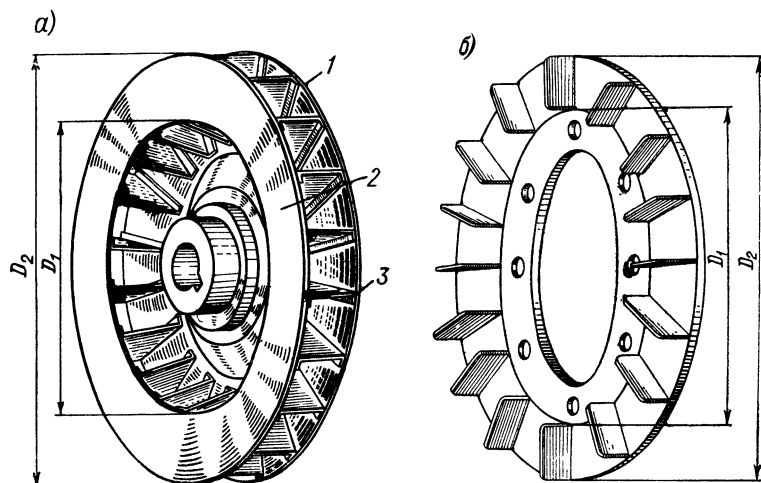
Рабочие колеса центробежного вентилятора: а — закрытое; б — с открытыми лопатками
